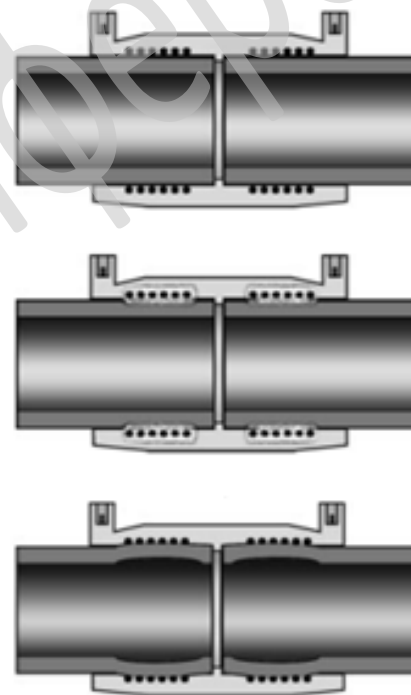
Сварка муфтой с закладным нагревателем
